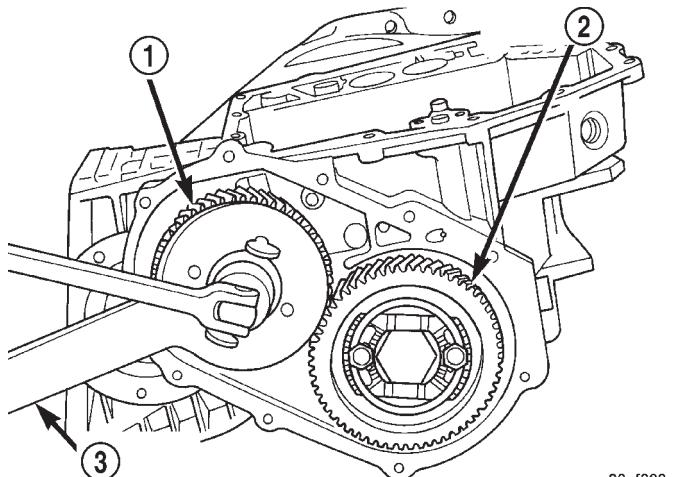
Desmontaje de la tuerca del engranaje del eje de transferencia
